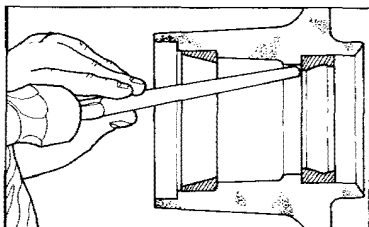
Удаление пробойником наружной обоймы подшипника из корпуса ступицы
